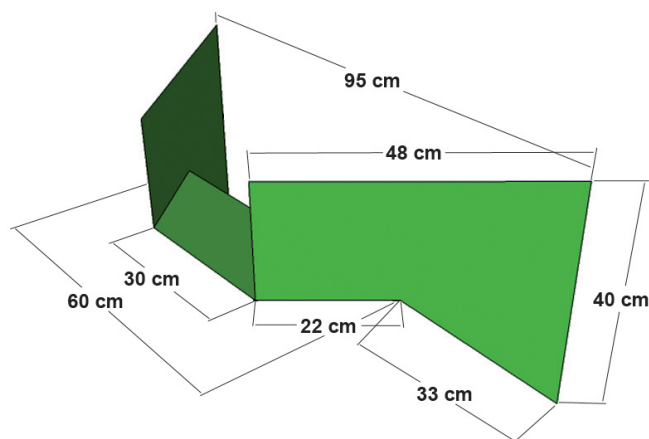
Detalhes da bica de descarga do tanque perfurado.
